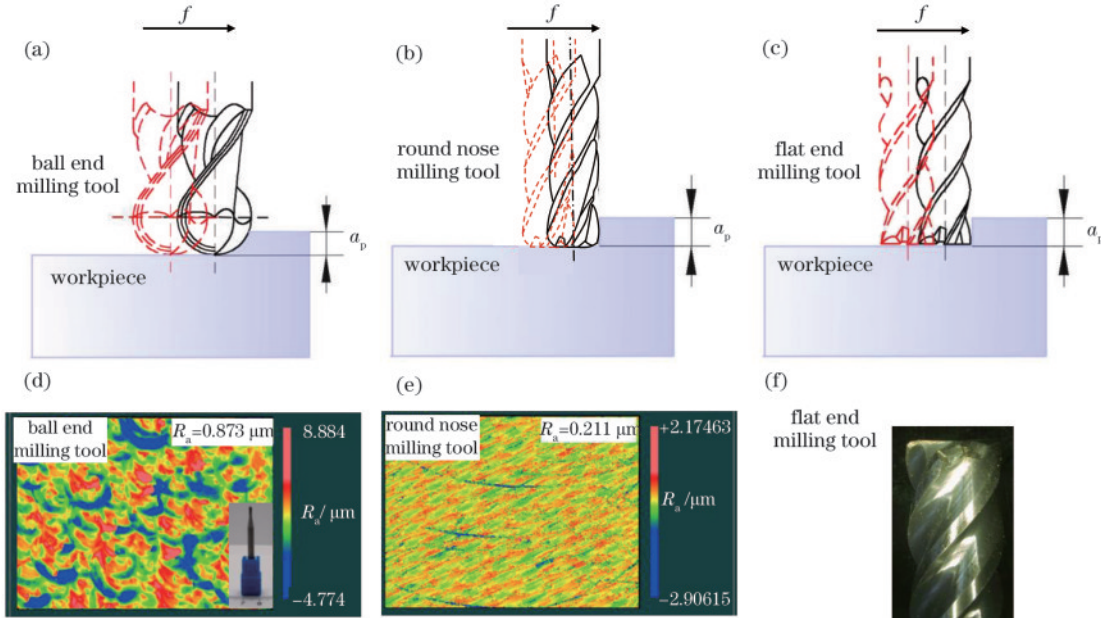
不同刀具铣削示意图及加工出的试样的表面粗糙度。(a) 圆鼻刀铣削示意图; (b) 球头刀铣削示意图; (c) 平头铣刀铣削示意图; (d) 球头刀加工试样的表面粗糙度; (e) 圆鼻刀加工试样的表面粗糙度; (f) 平头铣刀崩刀特征图
